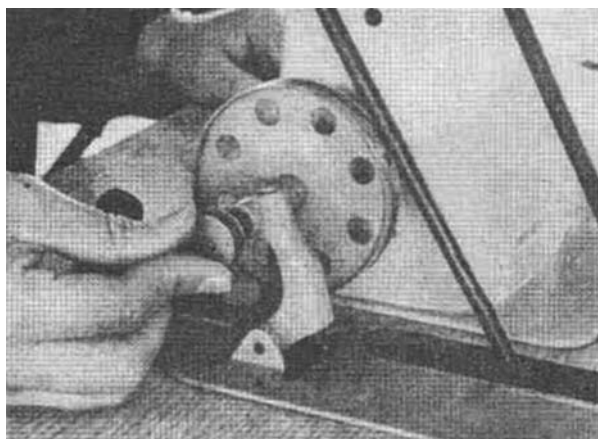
Установка шпульки на ось приспособления для намотки нити
